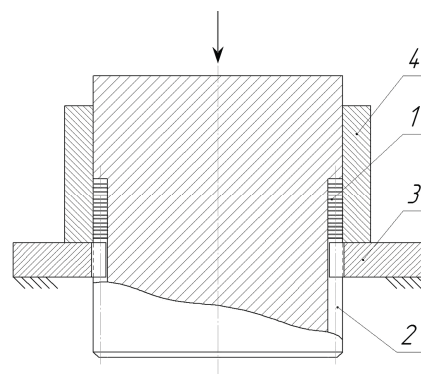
Операция осевого сжатия зубчатой ленты в пресс-форме: 1 – зубчатая лента; 2 – пуансон; 3 – матрица; 4 – оправка
